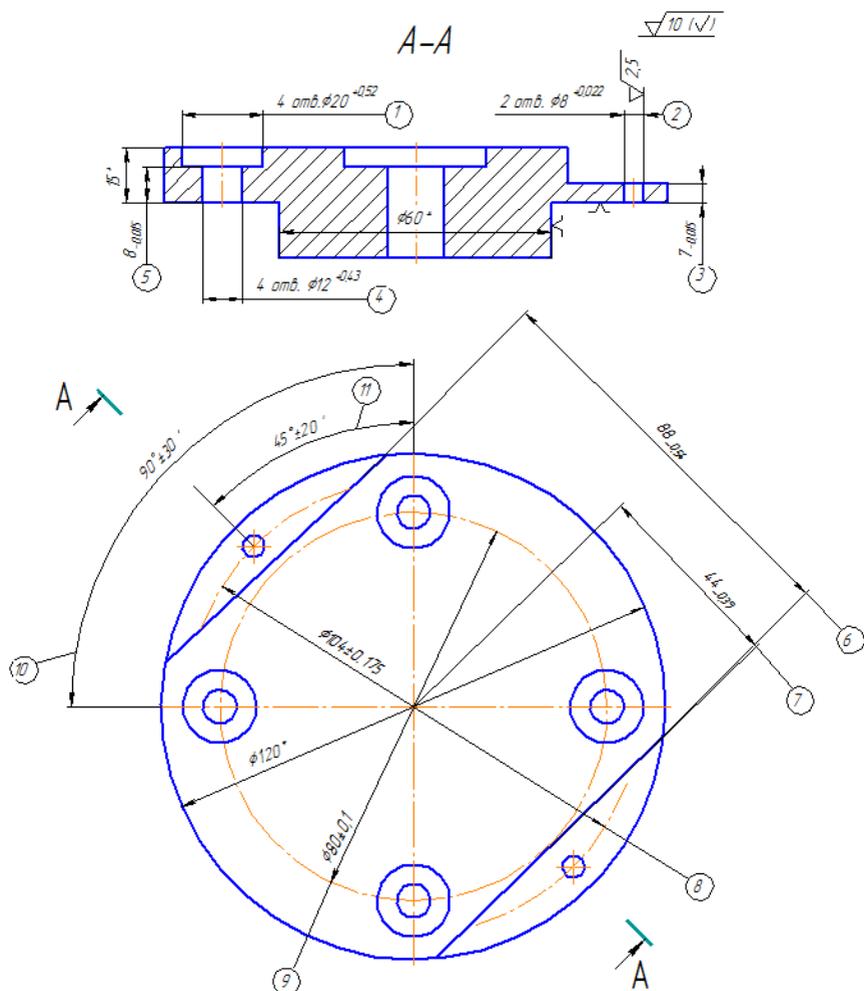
Эскизы заготовки и сверлильно-фрезерной операции обработки детали «Крышка» на станке модели 2254ВМФ4
